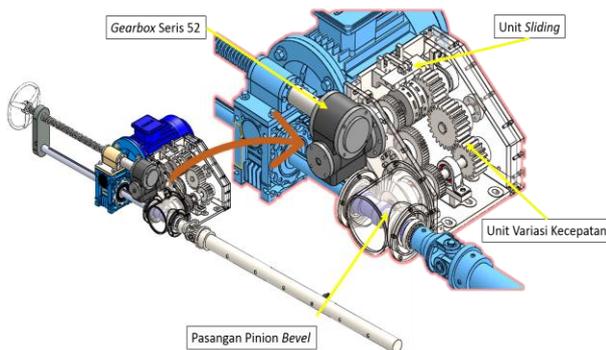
adalah desain 3D mesin *line boring* manual. Komponen penggerak pemakanan mesin ini adalah motor. Pertama, Daya motor dengan kecepatan rotasi 1440 rpm, kemudian direduksi melalui *gearbox* dengan kecepatan 36 rpm. Kedua, daya diteruskan pada boring bar dan pahat melalui *universal joint*. Daya inilah yang digunakan untuk pemakanan benda kerja. Ketiga, *handle* diputar oleh operator sehingga *leadscrew* ikut berputar. Rumah *leadscrew* berada dalam keadaan statis sehingga mekanisme pemutaran *leadscrew* membuat *nut adapter* bergerak maju dan mendorong pemakanan.
